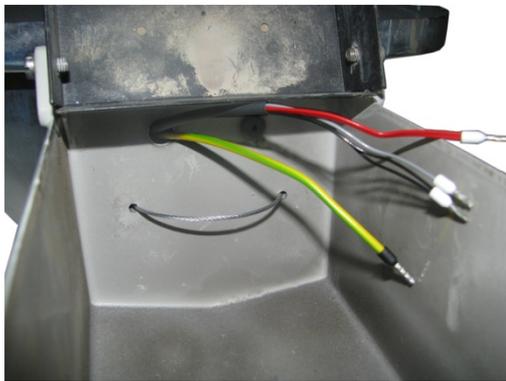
Detalle de montaje del kit cable acero y paso de cables del módulo óptico
